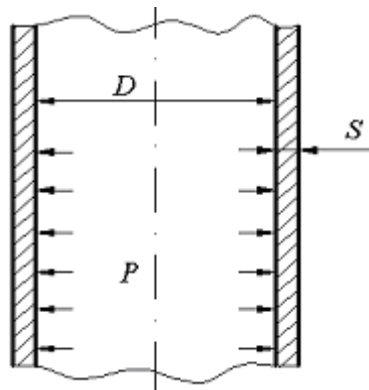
Розрахункова схема циліндричної обичайки
